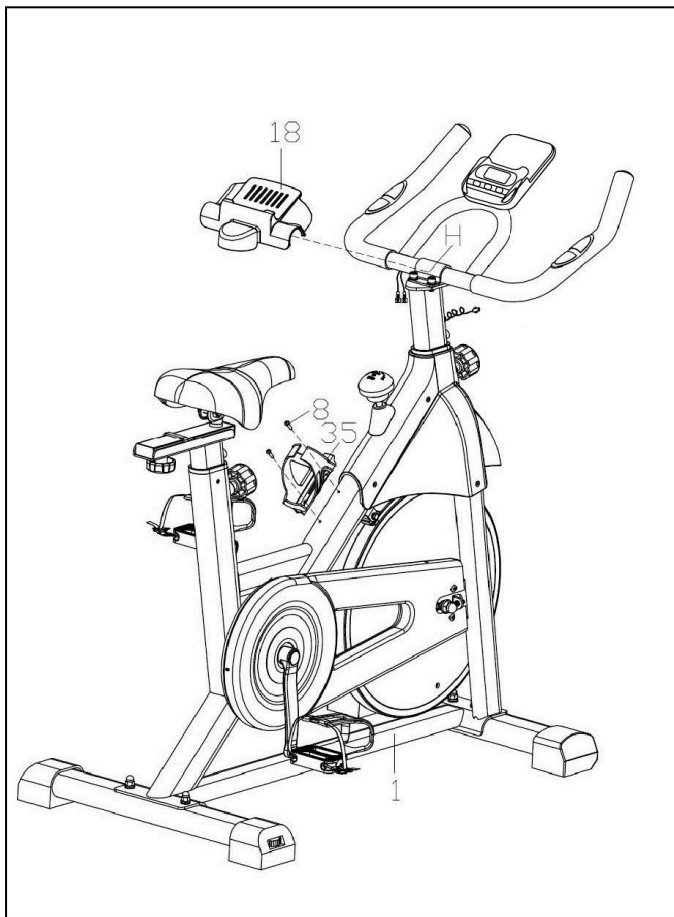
Установка держателя бутылки и кожуха поручней
